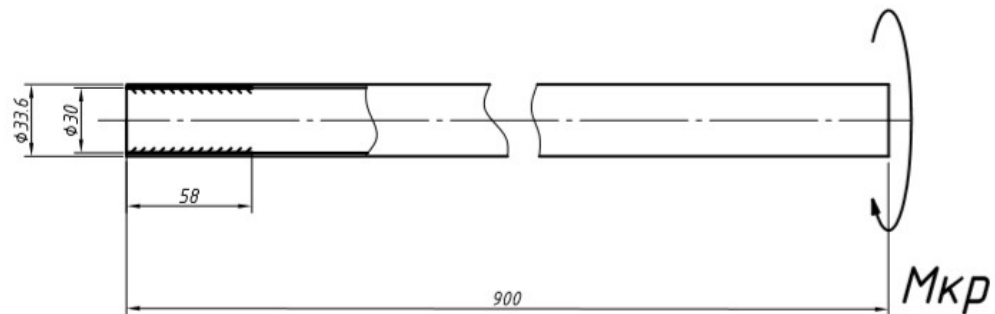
Розрахункова схема карданного валу нової конструкції третього типорозміру
